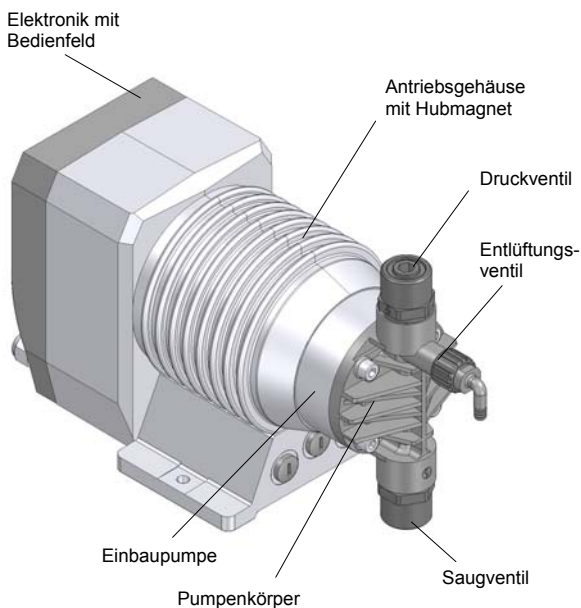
(Baugruppen der Magnet-Membranpumpe)
